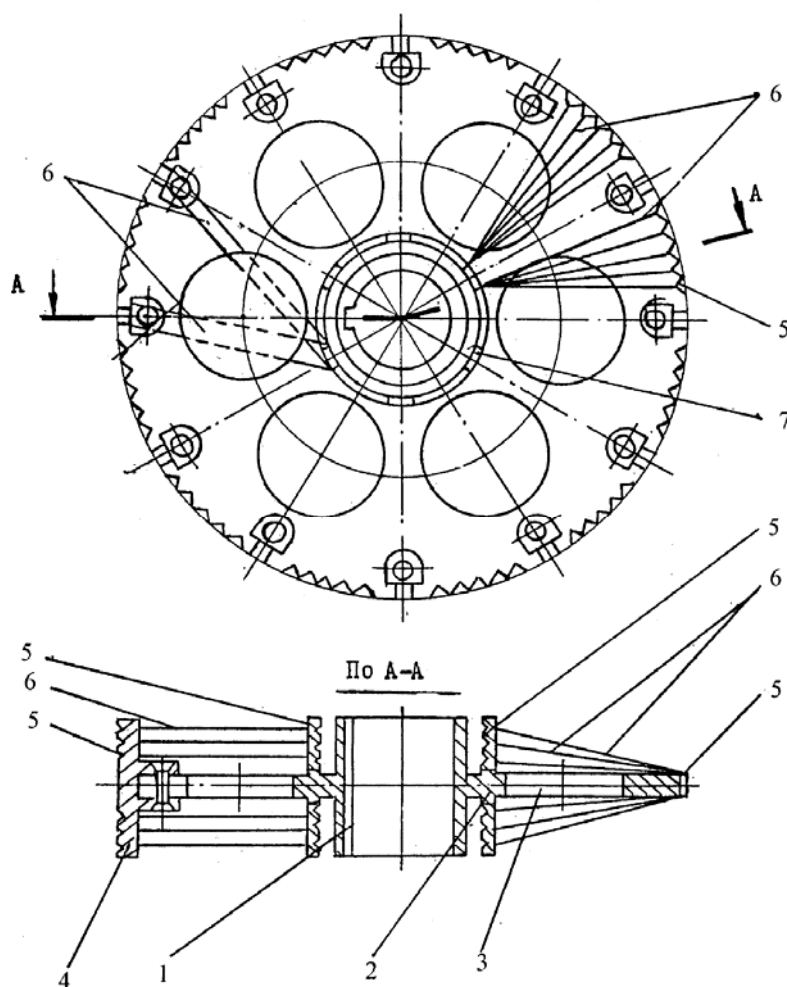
Общий вид колеса со струнными элементами центробежного насоса-мешалки и разрез А-А
